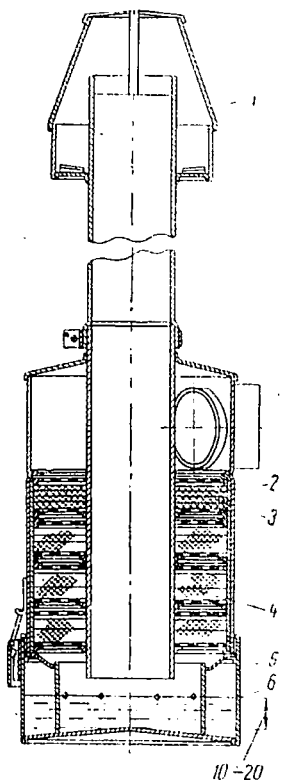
Воздухоочиститель компрессора станции ПР-10
